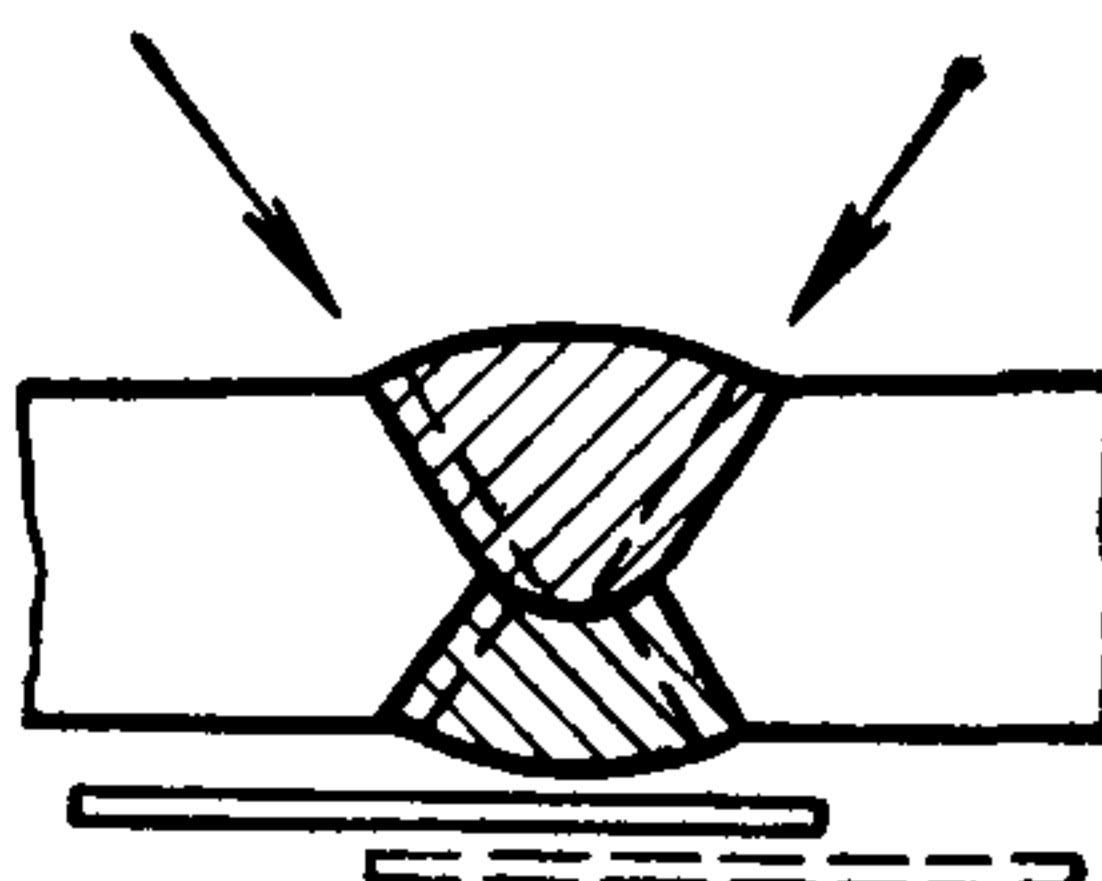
Схема просвечивания сварных стыков с X-образной подготовкой кромок для обнаружения дефектов по скосу кромок
